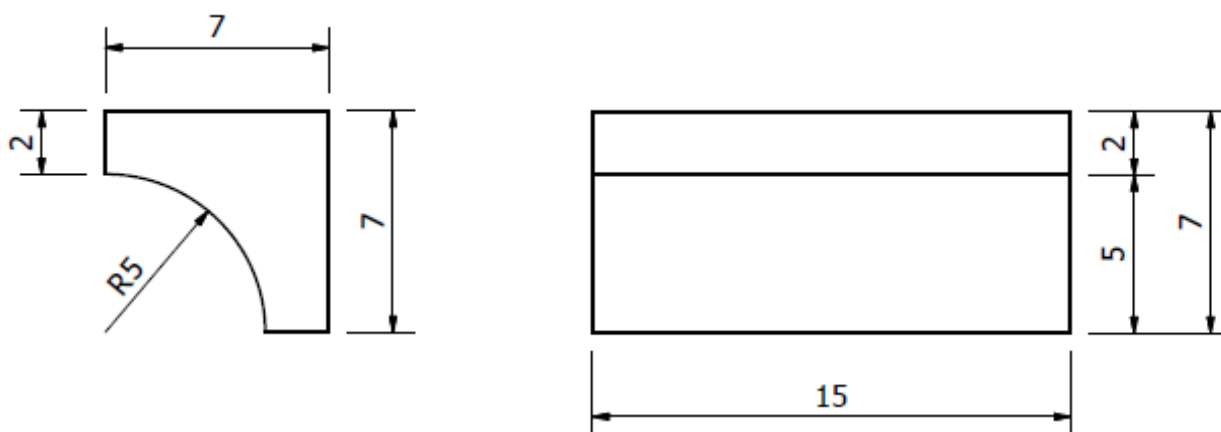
Perfil y alzado de las repisas destinadas a posadero
